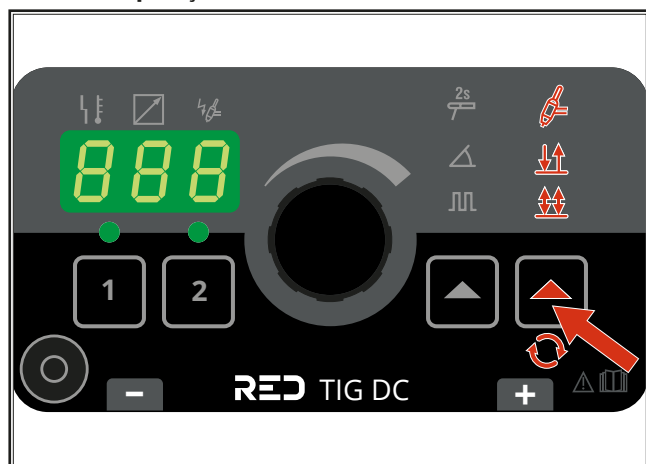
Ajustar o processo de soldagem e o modo de operação
